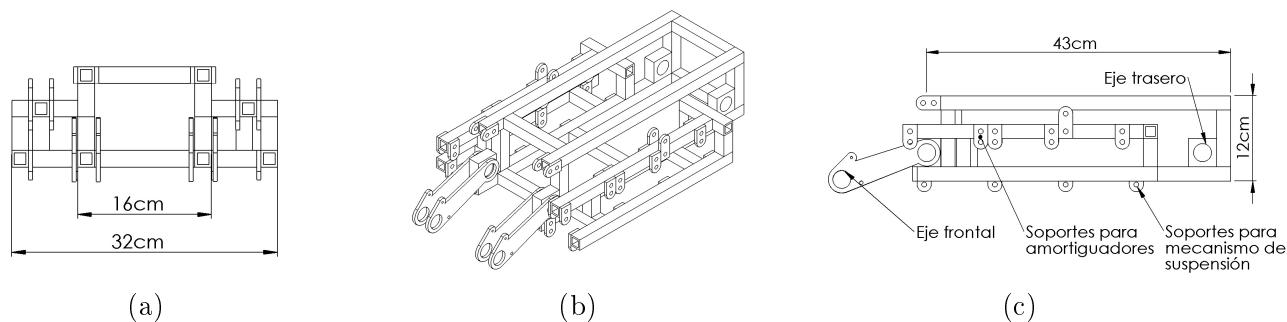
Chasis preliminar (a) vista frontal (b) vista isométrica (c) vista lateral.
